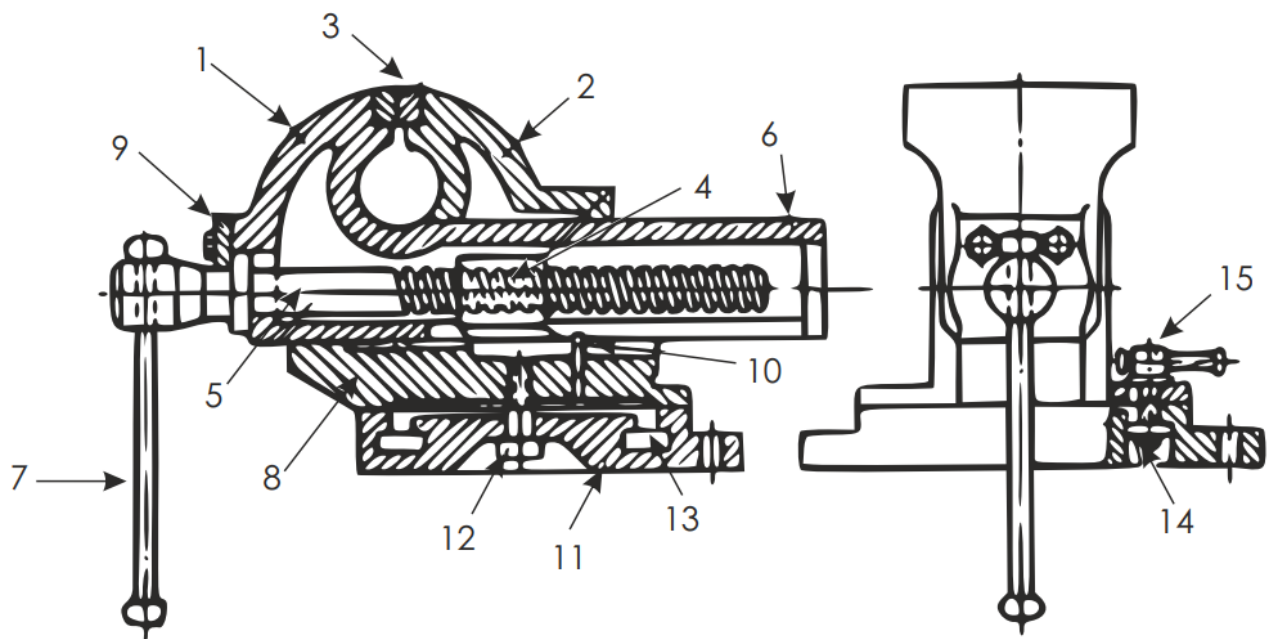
Поворотні паралельні лещата: 6 – рухома губка, 2 – нерухома губка, 3 – накладки, 4 – ходова гайка, 5 – ходовий гвинт, 1 – хвостовик рухомої губки, 7 – важіль, 8 – поворотна частина, 9 – стопорна планка, 10 – конічний штифт, 11 – плита, 12 – центровий болт, 13 – виточка для затискного гвинта, 14 – затискна гайка, 15 – болт з важелем
